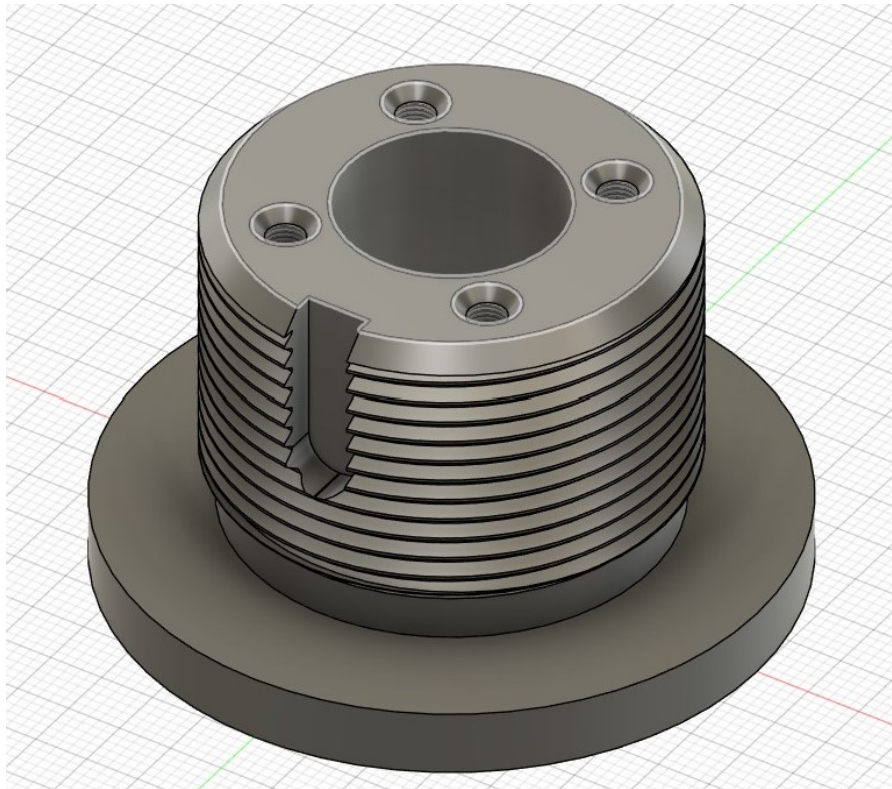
3D модель деталі «Втулка різьбова 8ВП.215.110»
